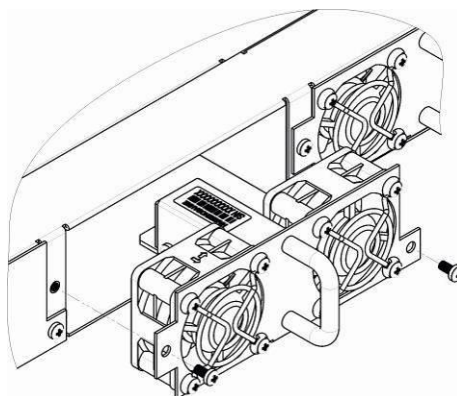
Блок вентиляции SMG-2016. Крепление в корпус
